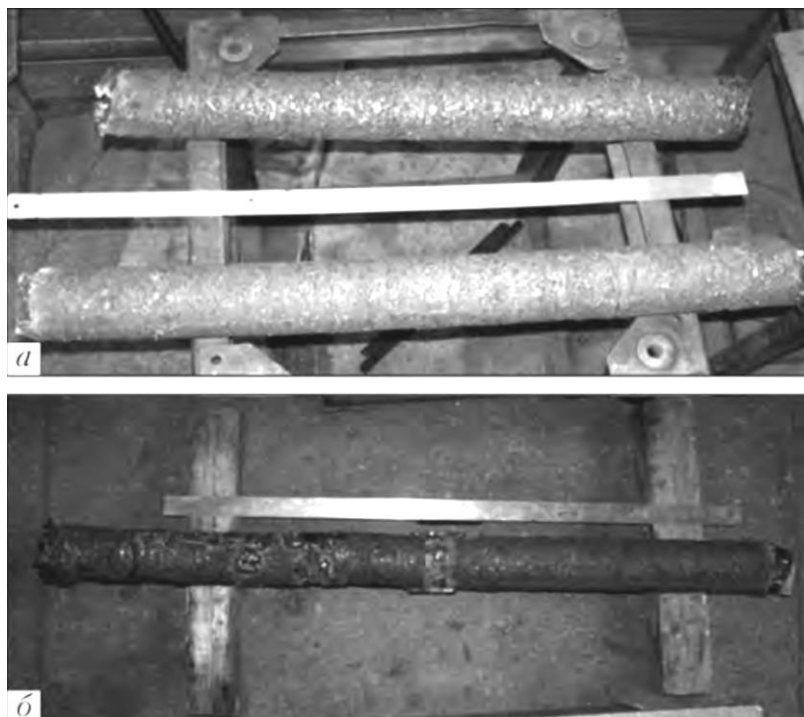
Получение электродов: а – из прессованной стружки ( $L=1000$  мм); б – сварно-спрессованная заготовка, собранная из двух прессовок ( $L=1880$  мм)
